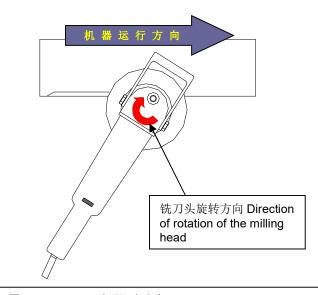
HDL-10A 机器运行方向 Machine running direction
